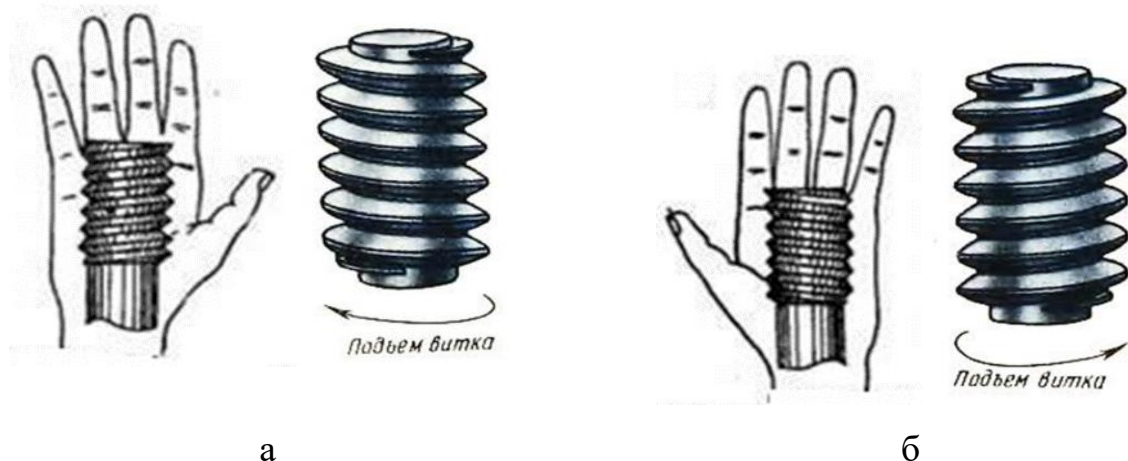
Направление навивки; а-правая резьба; б - левая резьба.
